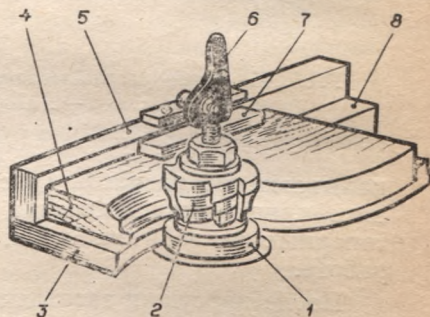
Обработка деталей с криволинейными кромками на фрезерном станке:
